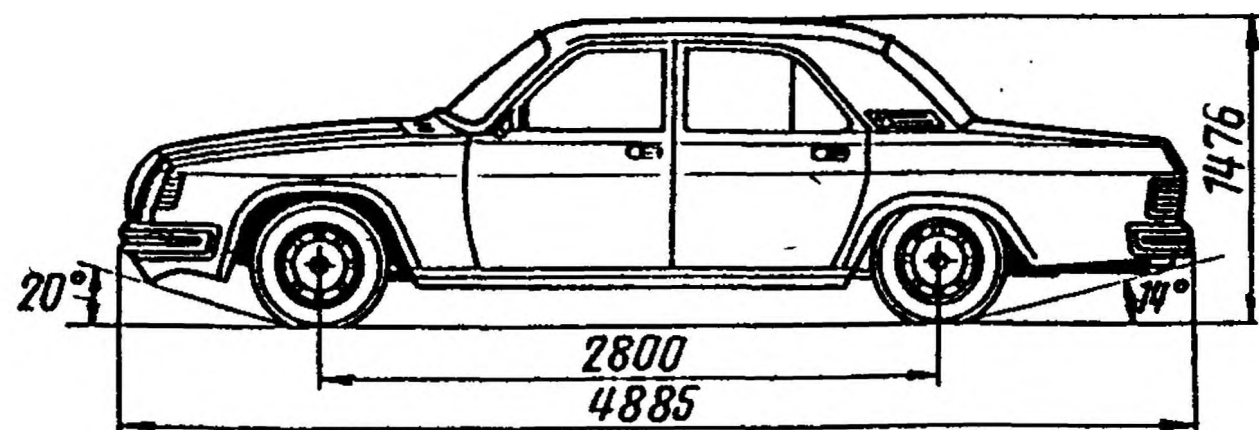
Автомобиль ГАЗ-31029. Габаритные размеры
